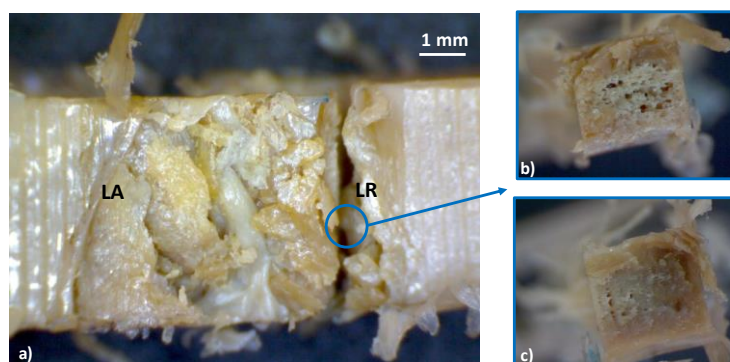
Macrografia do provete após Ensaio 6: a) Superfície superior do provete, b) Superfície de fratura do cordão de soldadura do LR, c) Superfície de fratura da interface do material base com o LR.
